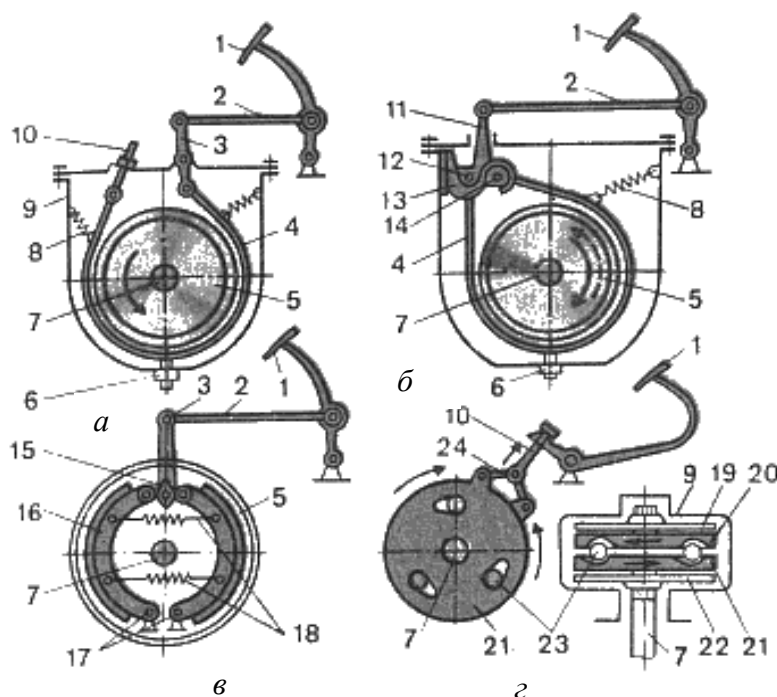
Схемы тормозных механизмов: а – простого ленточного; б – плавающего ленточного; в – колодочного; г – дискового; 1 – педаль; 2 – тяга; 3 и 11 – рычаги; 4 – тормозная лента; 5 – тормозной шкив; 6 – винт; 7 – вал; 8 – оттяжная пружина; 9 – картер; 10 – тяга с регулировочной гайкой; 12 и 14 – пальцы; 13 – неподвижный кронштейн; 15 – разжимной кулачок; 16 – колодка; 17 – неподвижные шарниры колодок; 18 – пружины; 19 и 22 – диски с фрикционными накладками; 20 и 21 – нажимные диски; 23 – шарики; 24 – серьга
